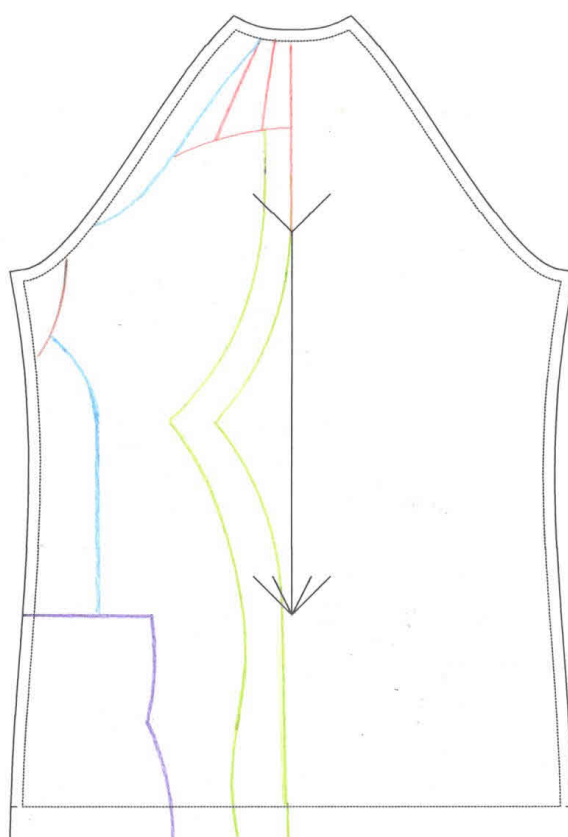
Výstup konstrukce PDS Tailor včetně konstrukčních bloků – přední díl, Zdroj: Pumax, spol. s r.o.
